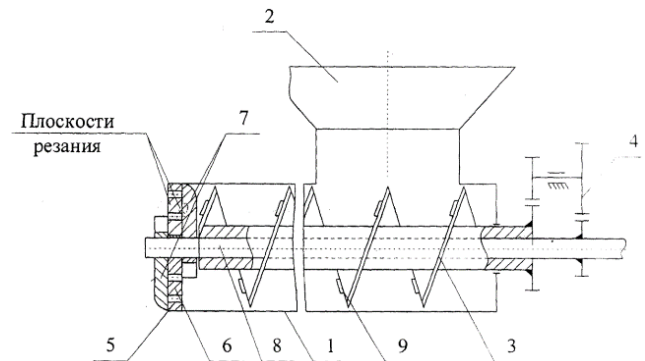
Универсальный шнеково-ножевой измельчитель сухих опилок в муку: 1 — корпус; 2 — бункер опилок; 3 — шнек; 4 — привод вращения шнека и вала; 5, 7 — ножи; 6 — решетка; 8 — вал ножей; 9 — захваты массы опилок
